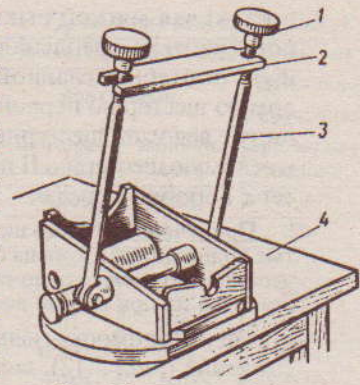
Приспособление для сборки и разборки коробки передач: 1 - винт; 2 - прижим; 3 - стойка; 4 - слесарный верстак
